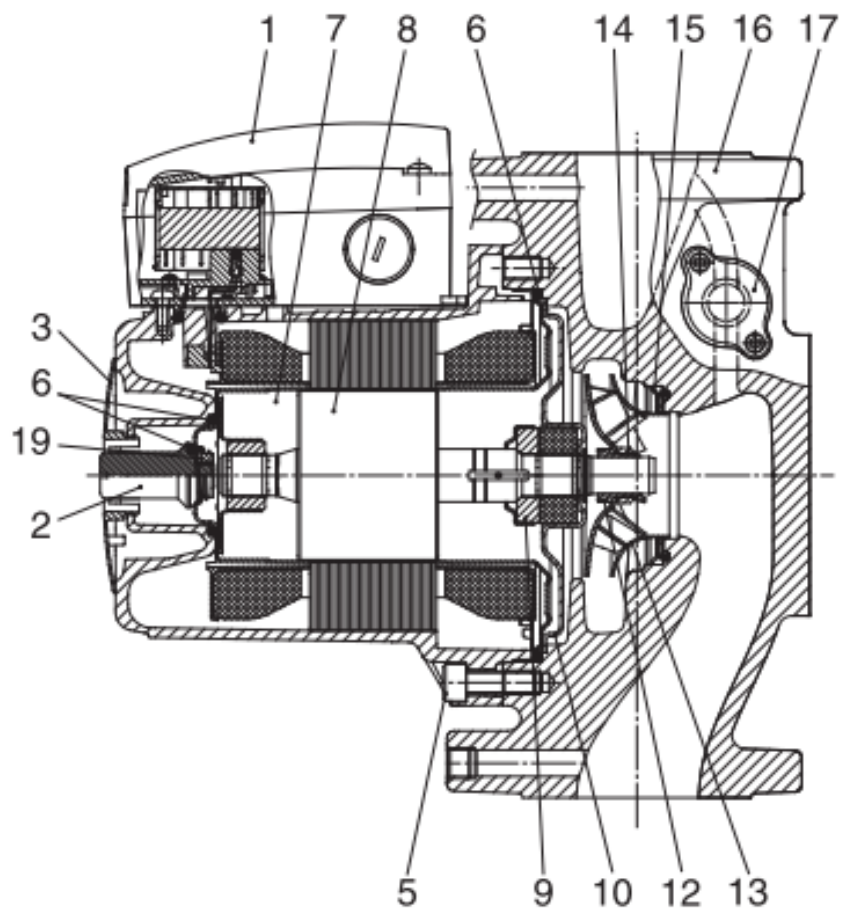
Принципиальная схема устройства насоса: 1 – клеммная коробка, 2 – резьбовая пробка, 3 – фирменная табличка, 4 – корпус статора, 5 – винты, 6 – уплотнительное кольцо, 7 – наружное кольцо, 8 – вал, 9 – упорный подшипник, 10 – подшипниковая пластина, 11 – стопорное кольцо, 12 – разрезной конус, 13 – рабочее колесо, 14 – гайка, 15 – щелевое уплотнение, 16 – корпус насоса, 17 – гнездо разъема датчика, 18 – поворотная заслонка, 19 – кольцо для защиты от брызг
